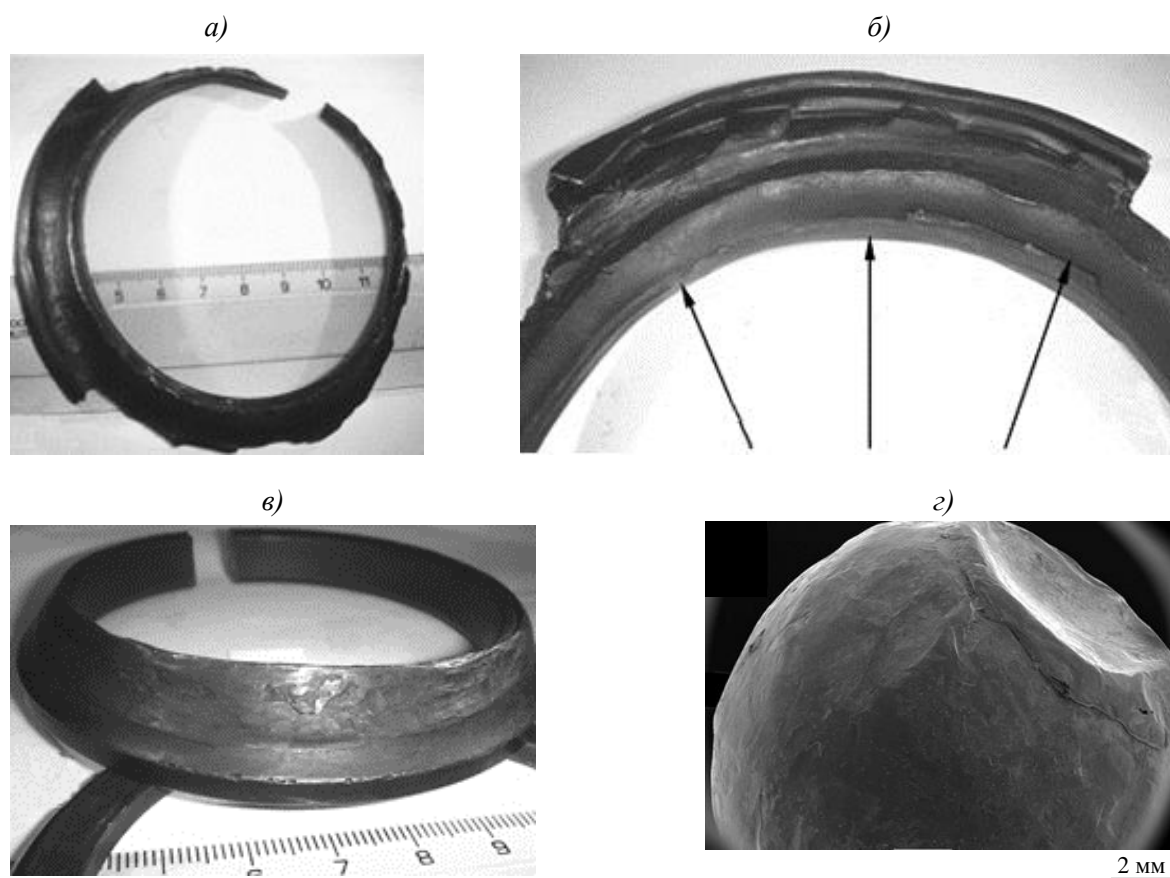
Внутренние полукольца шарикового подшипника из стали ШХ15:
